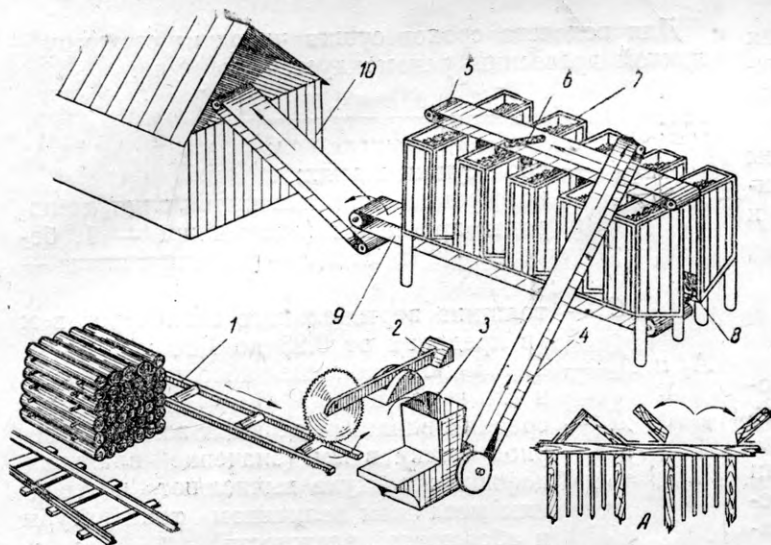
Схема цеха для заготовки и сушки газогенераторных чурок
